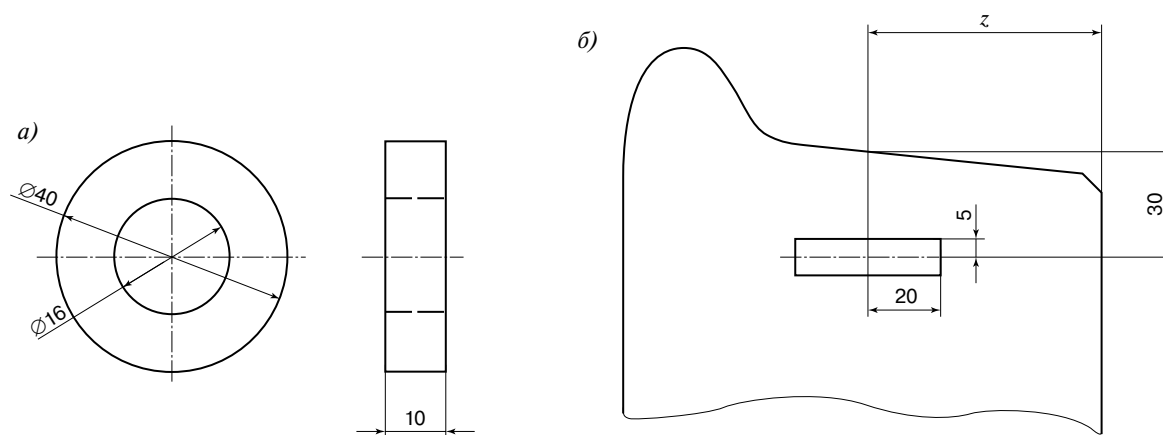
Эскиз ролика для испытаний на износ (а) и схема вырезки из банджа ролика для испытаний на износ (б): z — $1/2$ ширины банджа
